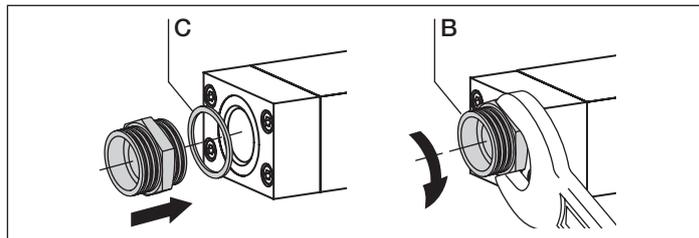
Dichtring anbringen und Anschlussgewinde anschrauben
